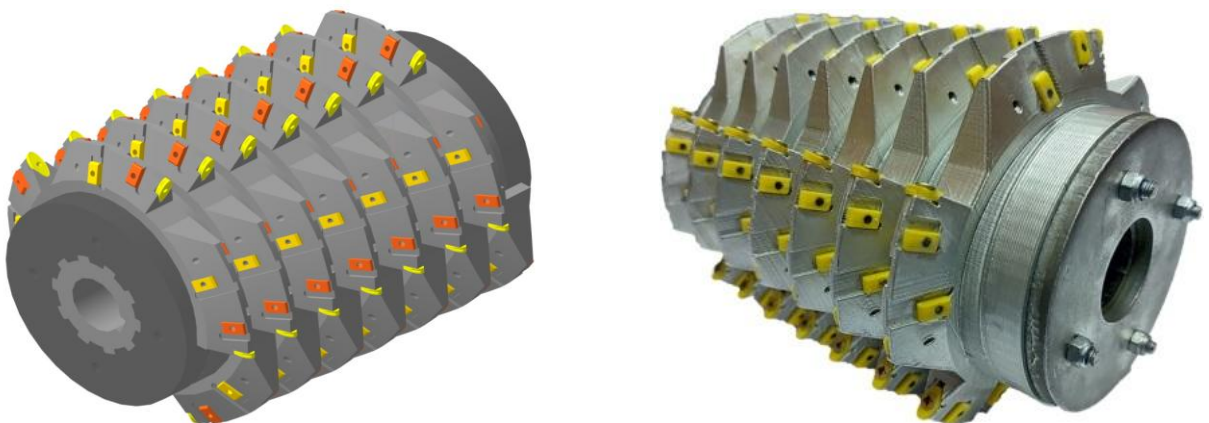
Конструкция сборной червячной фрезы с групповым расположением РЭ (патент на изобретение № 2720011)
